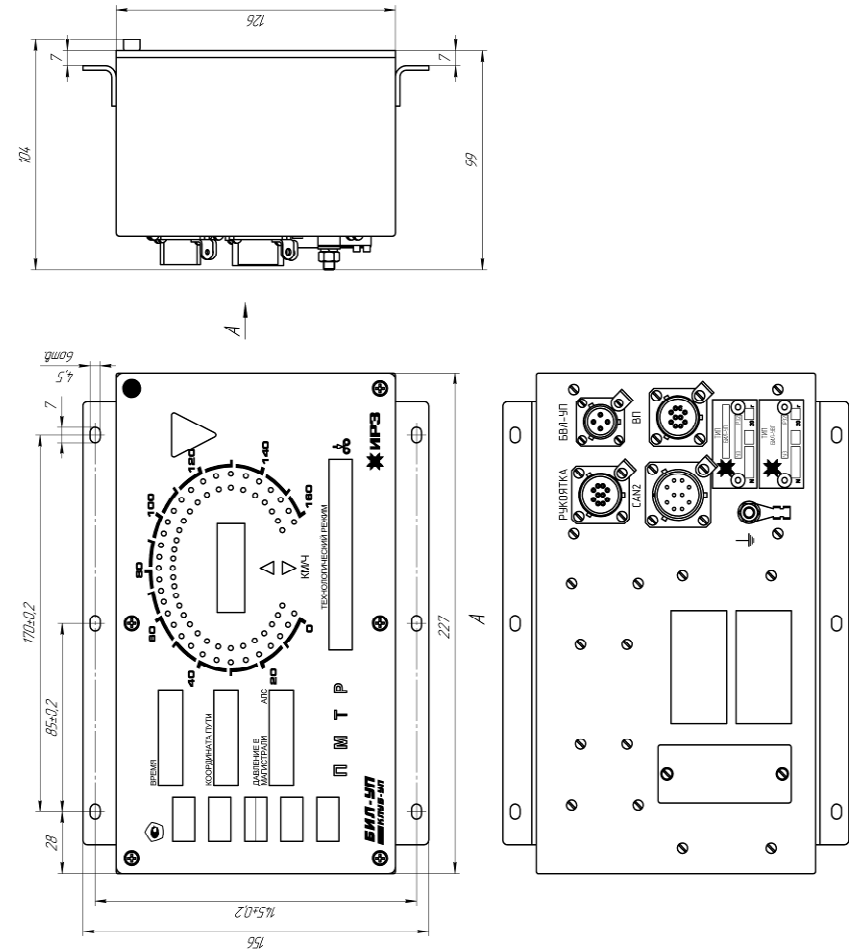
Внешний вид и габаритные размеры блока БИЛ-УП-01 36993-310-00-01
